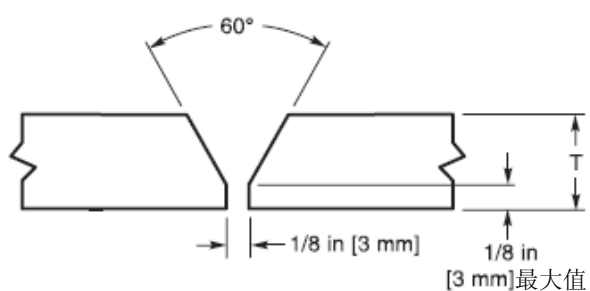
管材 (无衬垫) 对焊接头 — 焊工资格评定用
